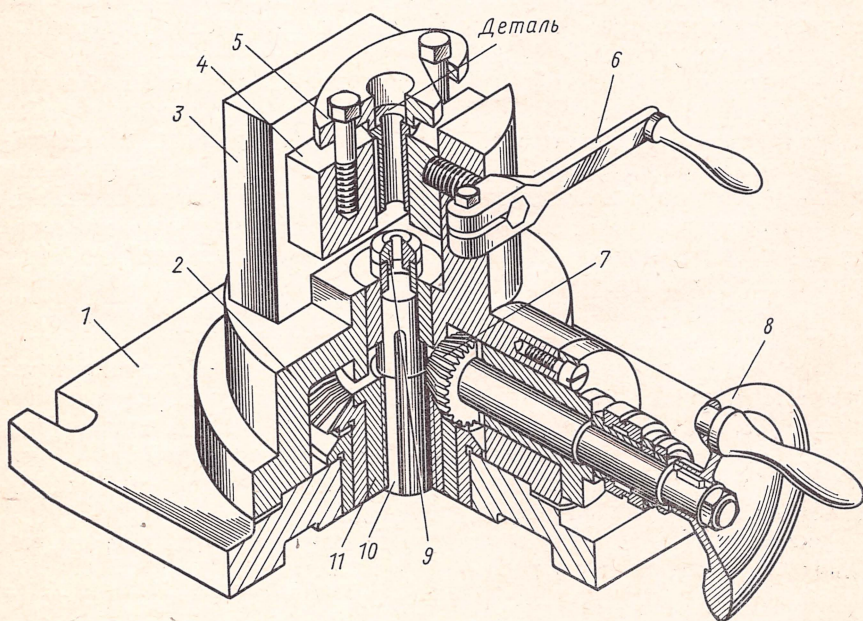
Приспособление для крепления гильзы плунжера топливного насоса на внутридодовочном вертикальном станке:
